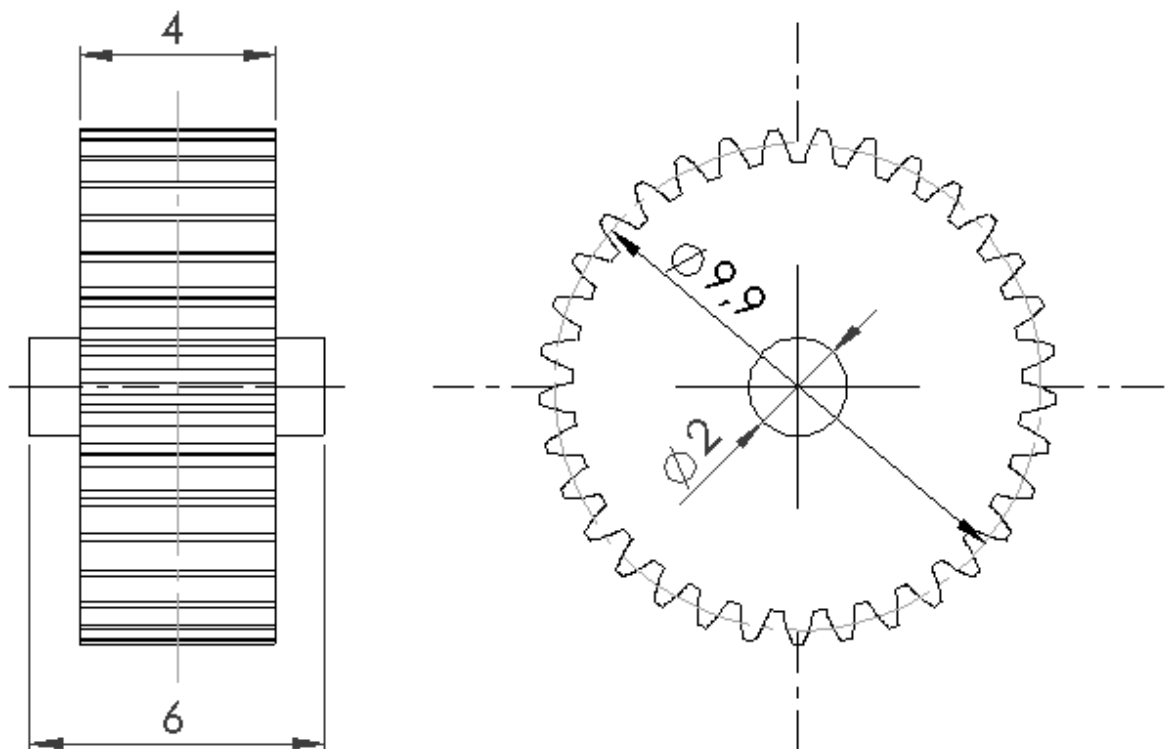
Dimensions principals de l'engranatge o pinyó. (Part A)
